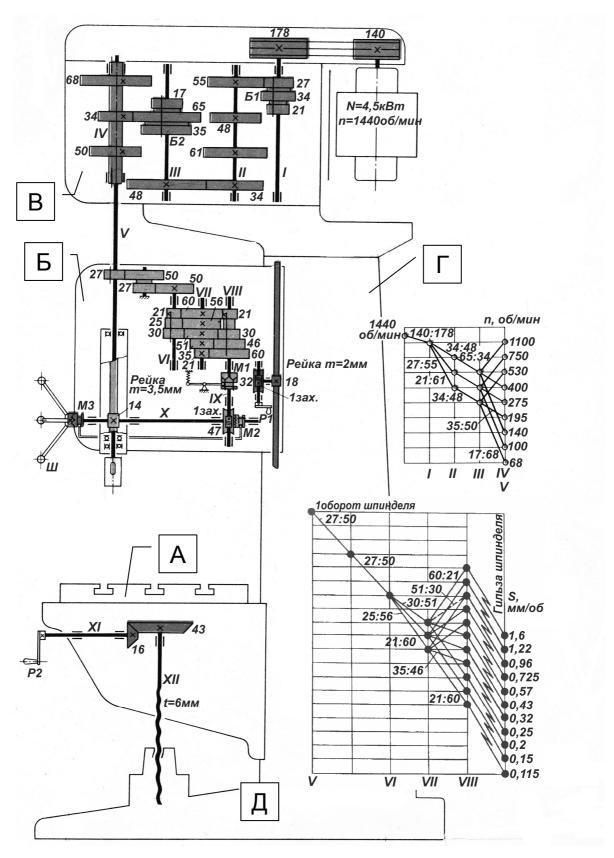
Кинематическая схема станка модели 2A135: А – стол станка; Б – шпиндельная бабка с коробкой подач и подъемным механизмом; В – коробка скоростей; Г – станина (колонна); Д – основание станины
